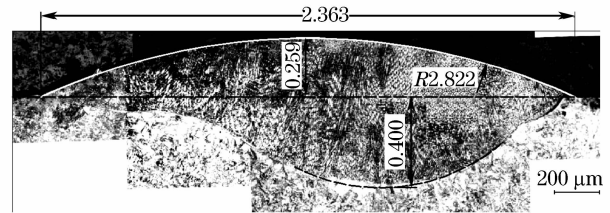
a 试样截面形貌轮廓模拟及尺寸标注
